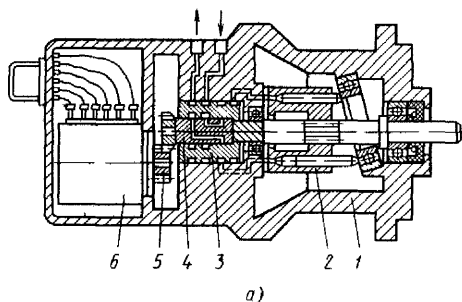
ЭГСА поворотного движения с ЧПУ:
